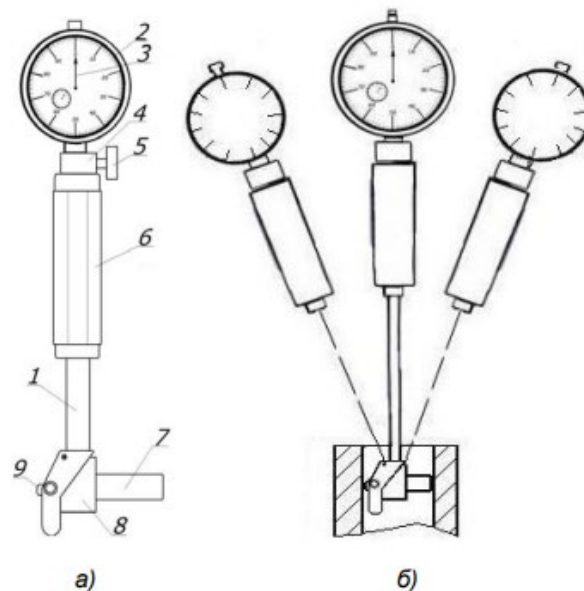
Индикаторный нутромер: а – общий вид; б – измерение нутромером размера детали
